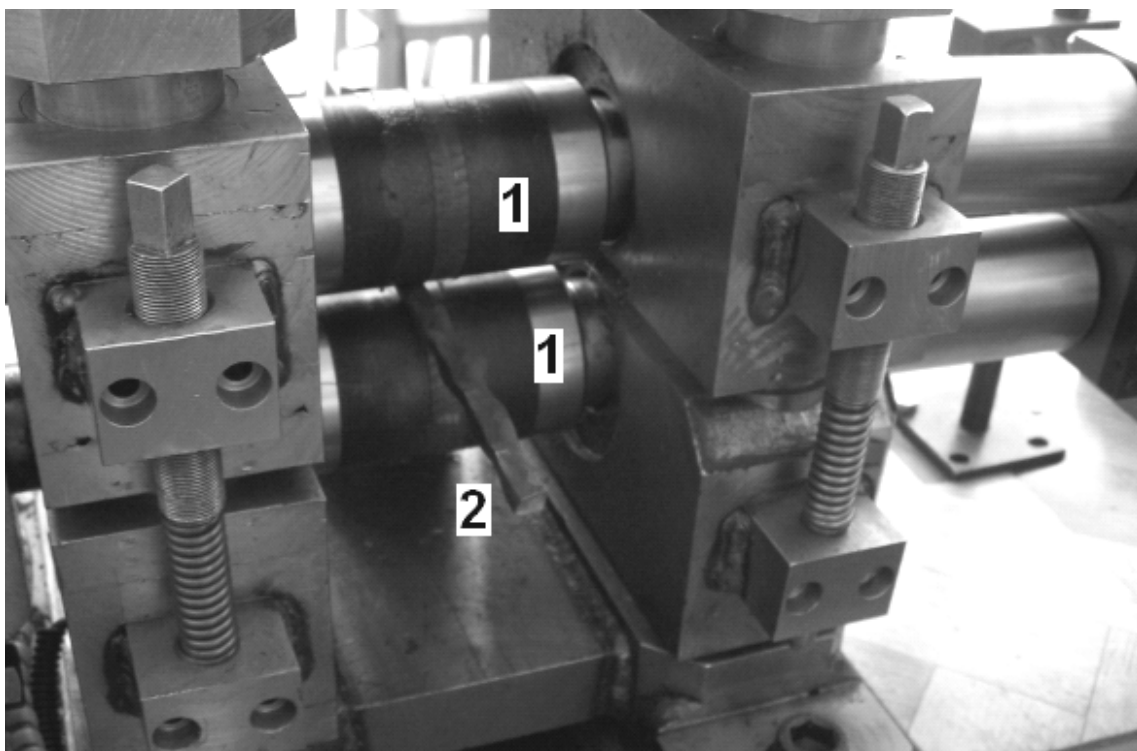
Экспериментальная установка: 1 – нижний и верхний валки, 2 – образец
